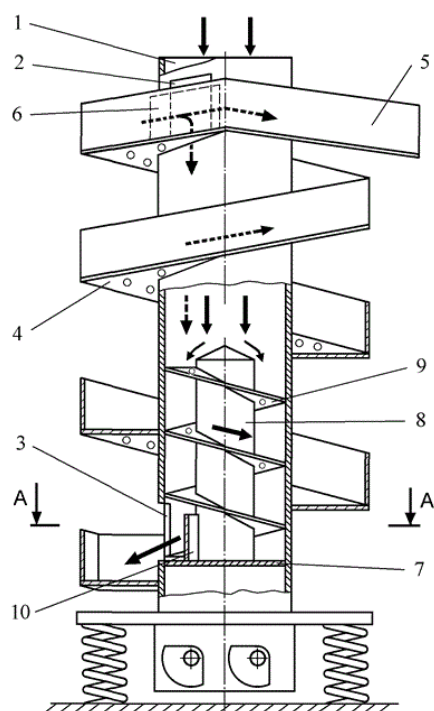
Вибрационный смеситель № 2. Общий вид: 1 — бункер; 2, 3 — отверстия; 4 — желоб; 5 — выгрузочный патрубок; 6 — подвижная заслонка; 7 — дно загрузочного бункера; 8 — цилиндрическая вставка; 9 — лопасть; 10 — неподвижная заслонка
